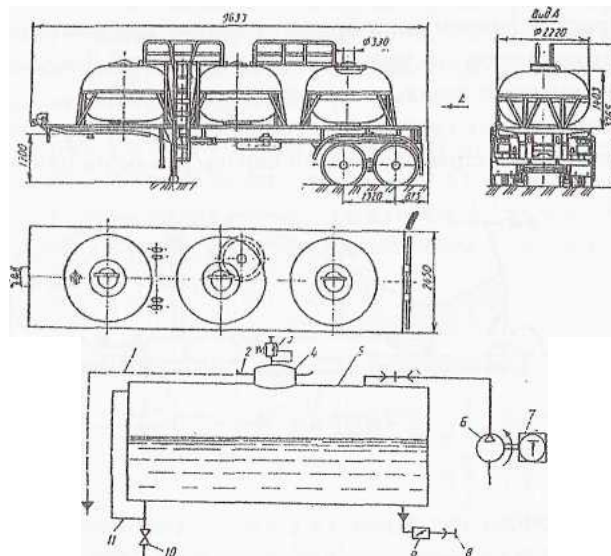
Принципова схема технологічного устаткування полу-причепи-цистерни ЕД-20,5-1 з мотокомпресором: 1 — зливна трубка; 2 — коритце; 3 — клапан; 4 — люк; 5 — цистерна; 6 - компресор; 7 — двигун внутрішнього згорання; 8 — швидкокорозійна муфта; 9 — затвор; 10 — кран; 11 — рівнемір
